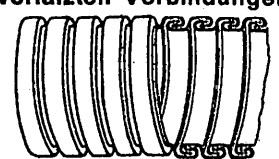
Schlauch mit mehrgängigem Gewinde.
